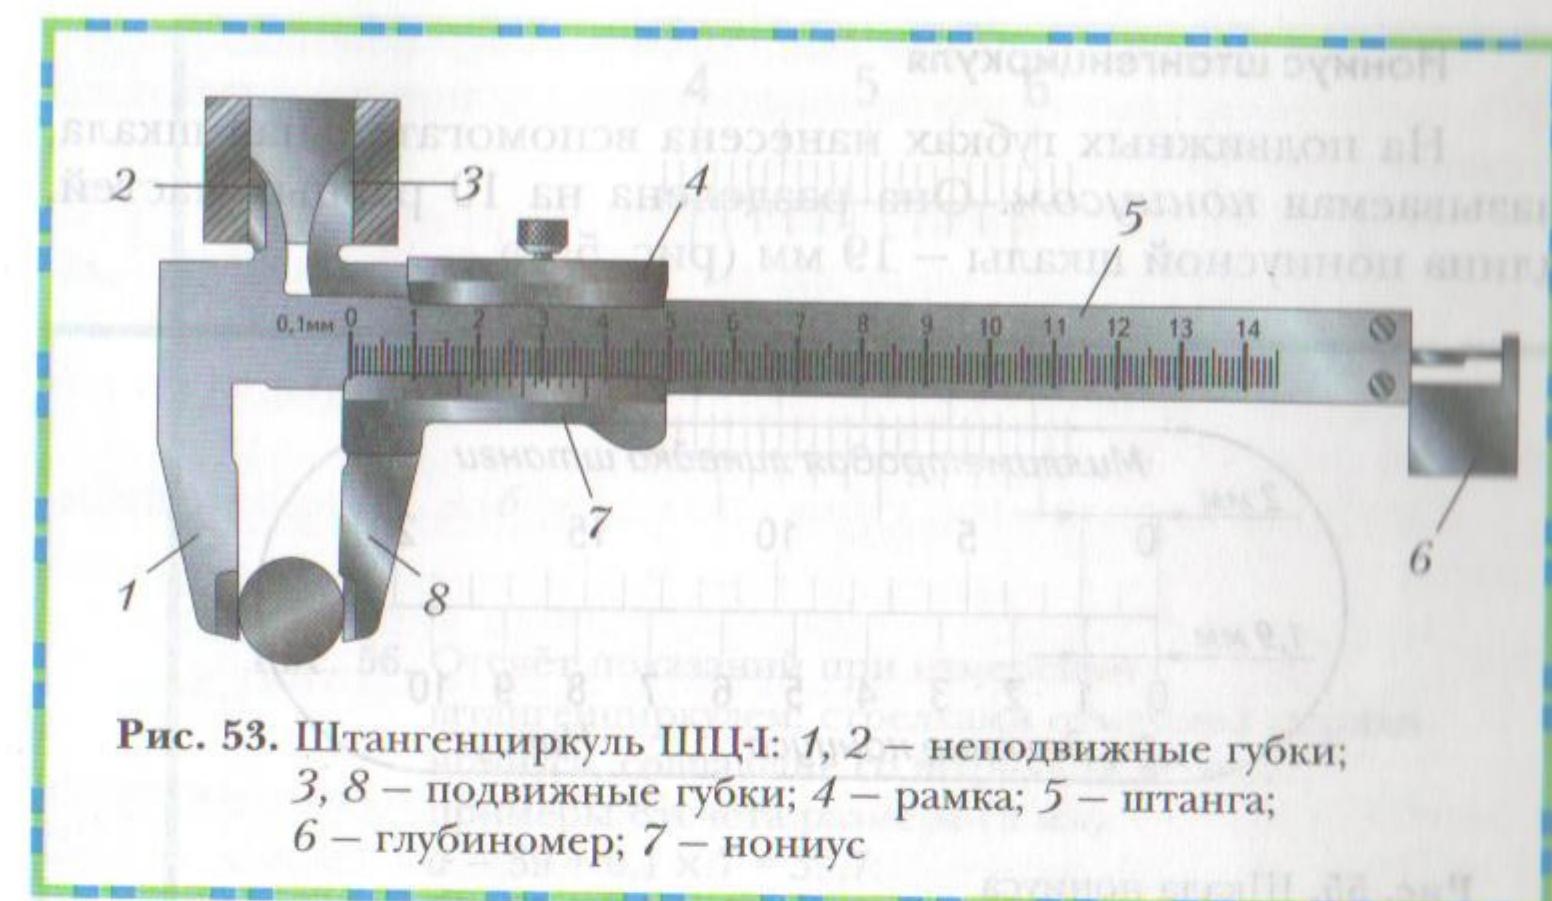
Штангенциркуль ШЦ-І: 1, 2 — неподвижные губки; 3, 8 — подвижные губки; 4 — рамка; 5 — штанга; 6 — глубиномер; 7 — нониус
